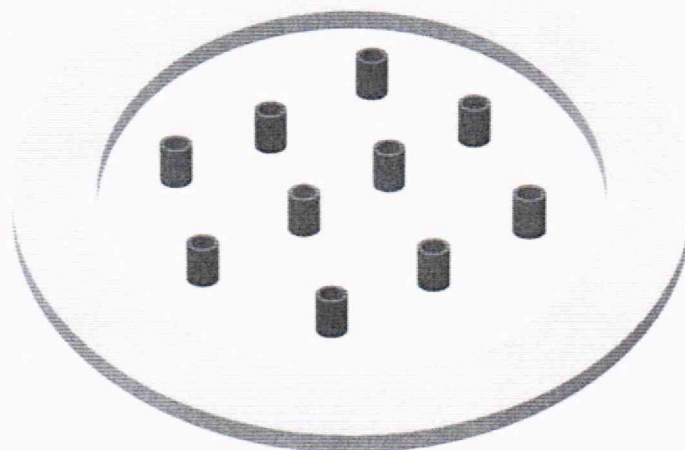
Схема установки алюминиевых втулок внутри вспомогательного кольца
